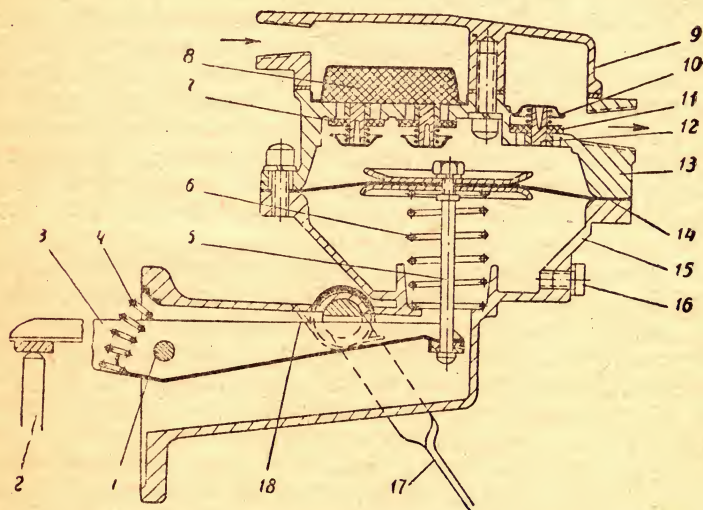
Топливный насос Б-9 двигателя ЗИЛ-130
